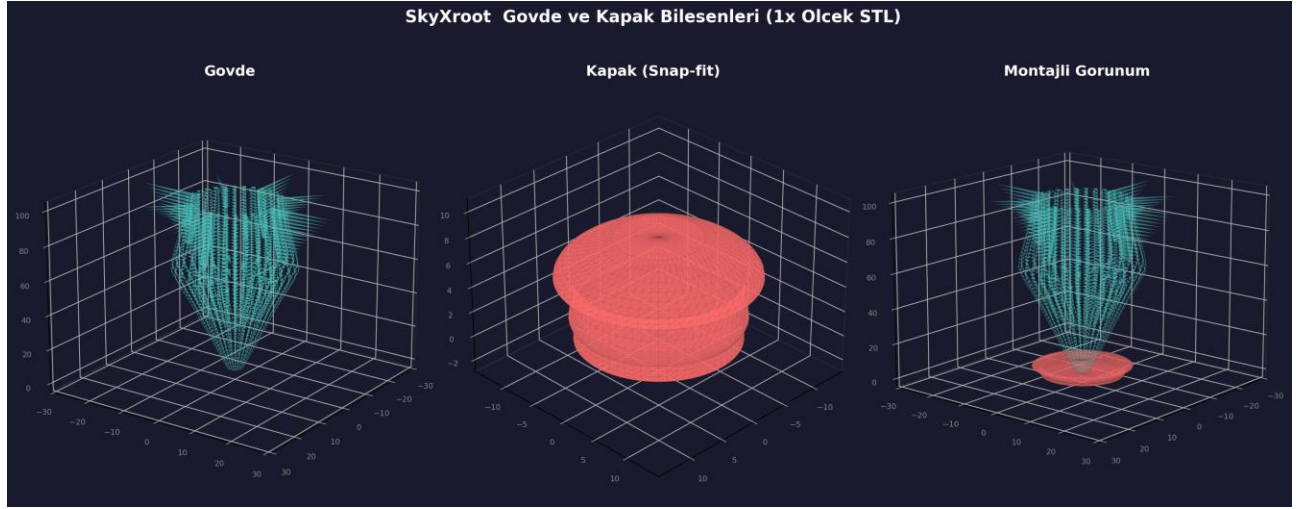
Corps, bouchon et vue assemblée créés à partir de fichiers STL (échelle 1x).
